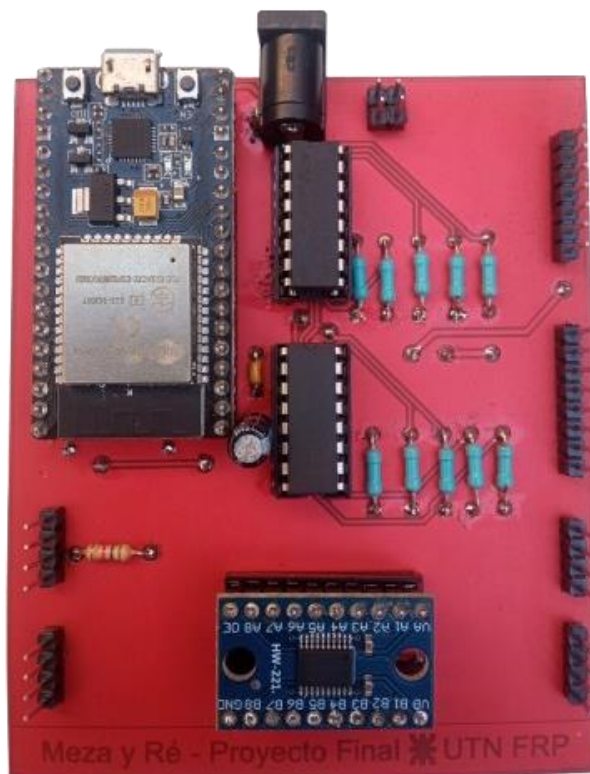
Diseño PCB- Placa finalizada TOP [fuente propia]
